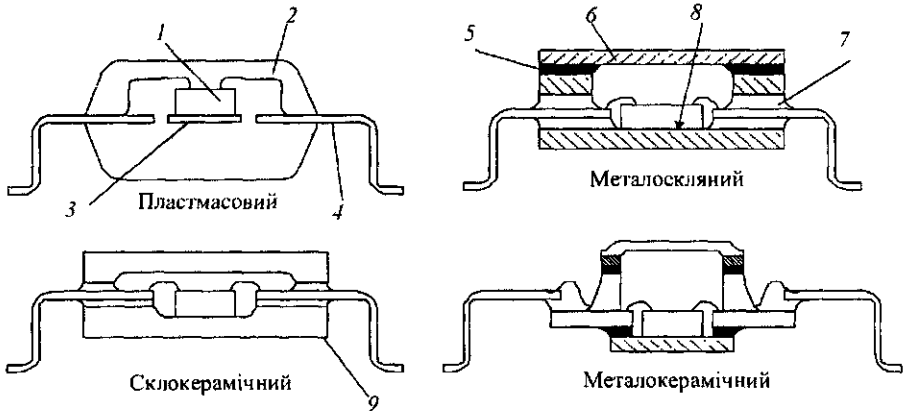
Конструкції корпусів ІМС: 1 — кристал ІМС; 2 — проводові провідники; 3 — кристалотримач; 4 — виводи; 5 — низько температурний припій; 6 — кришка корпусу; 7 — скло (склоприпій); 8 — монтажна площадка; 9 — основа корпусу
